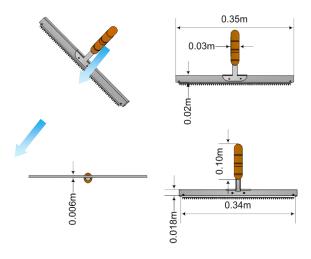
Vistas dimensionadas de la herramienta de corte manual.
